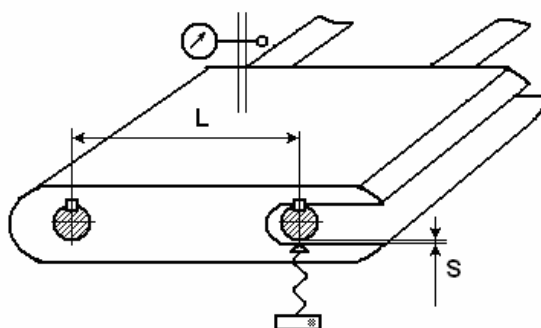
Цилиндрическая направляющая с двумя валами.
